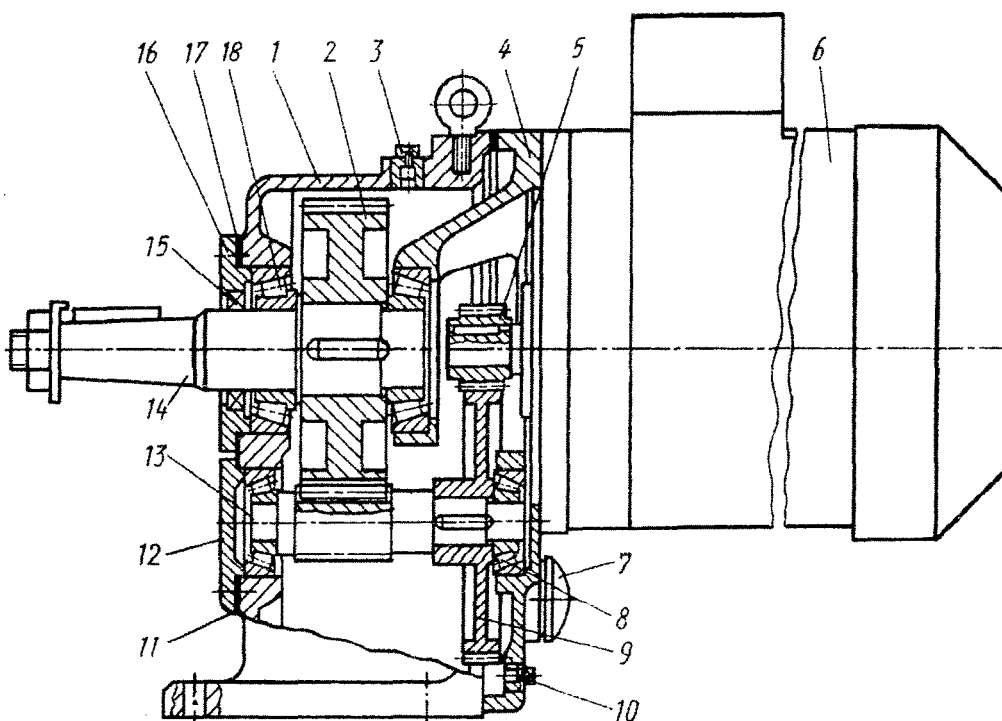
Двухступенчатый цилиндрический соосный мотор-редуктор
